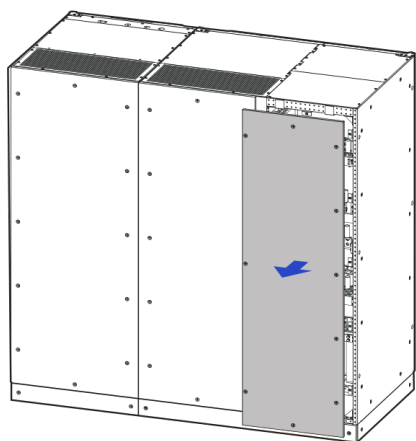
Retiro de las cubiertas de cableado del UPS-IND HF 13800
